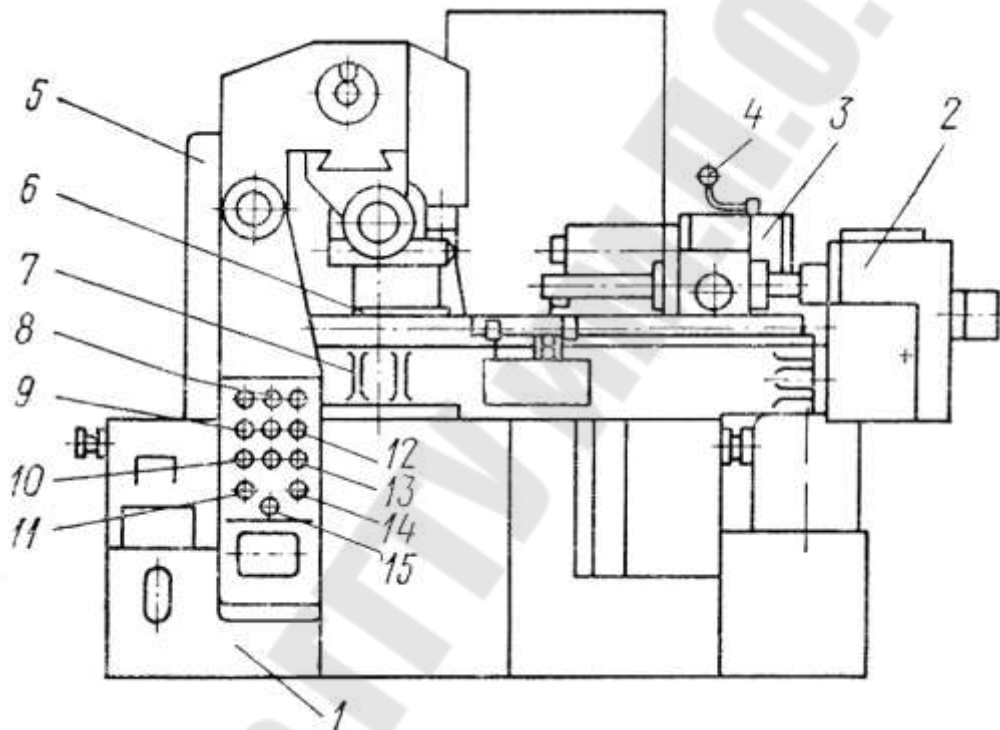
Эскиз специального фрезерного полуавтомата модели СИ-017: 1 – станина; 2 – механизм подачи стола; 3 – шпиндельная бабка; 4 – рукоятка отвода шпиндельной бабки; 5 – фрезерная бабка; 6 – стойка; 7 – стол; 8 – лампочка «Напряжение»; 9 – кнопка «Насос»; 10 – кнопка «←»; 11 – переключатель «Зажим–Отжим»; 12 – кнопка «Цикл»; 13 – кнопка «→»; 14 – переключатель режим работы; 15 – кнопка «Стоп»
